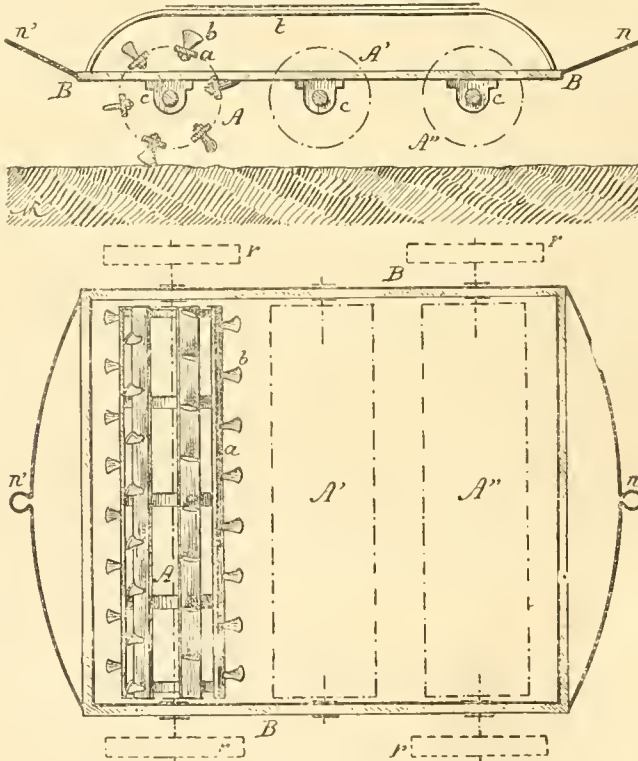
Elevation et plan d'un trilho (Veuve Theotonio Jose Xavier).
